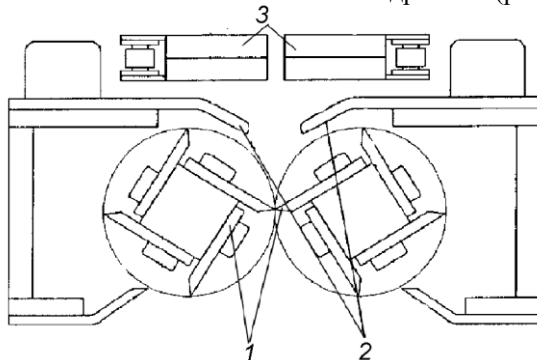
Схема качано-відокремлювального апарата з планчатими ножами: 1 – ротор з планчатими ножами; 2 – стріперні пластини; 3 – подавальні ланцюги
